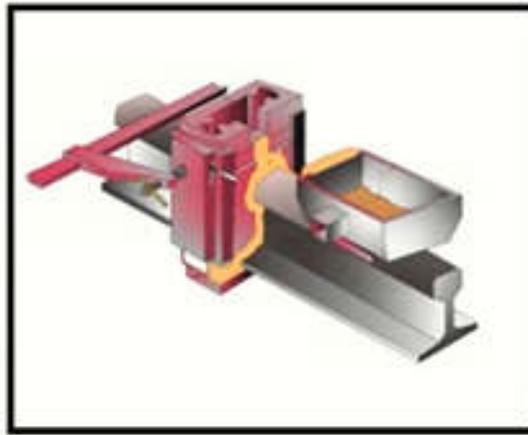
Accesorios y equipamiento utilizados para la soldadura por aluminotermia
